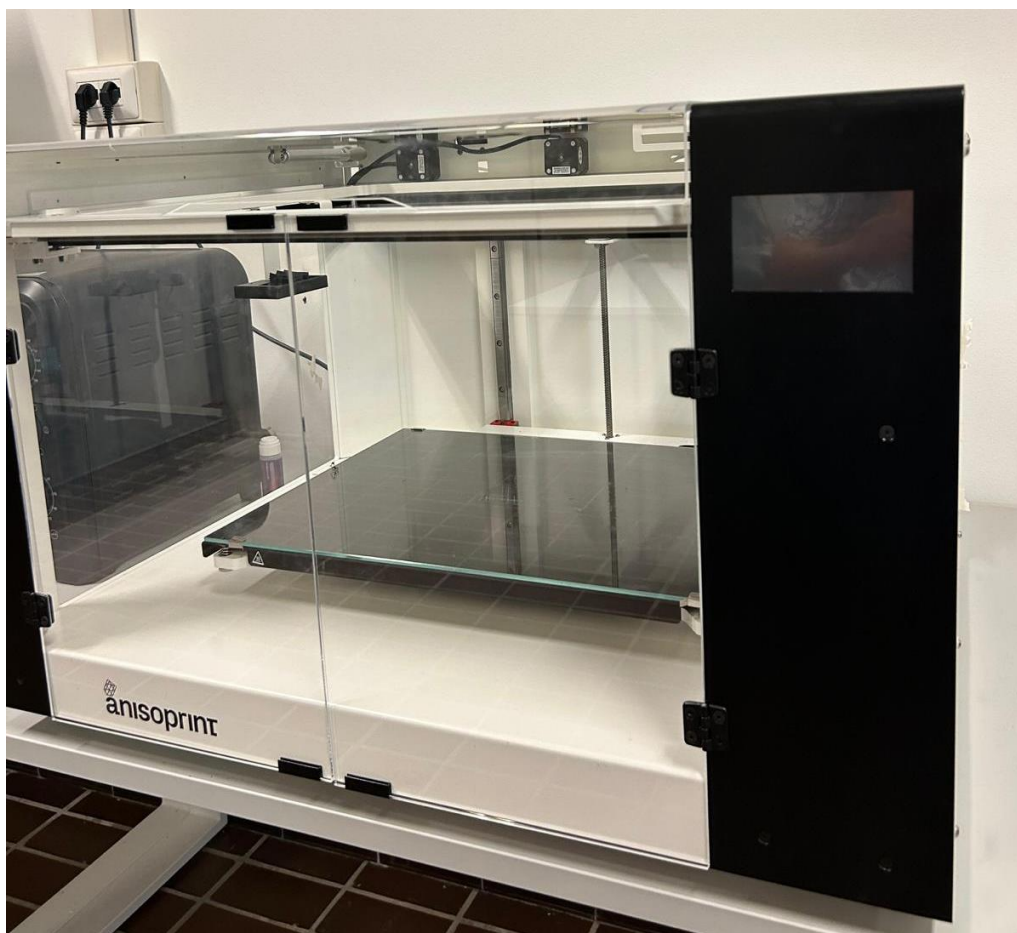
Frontale dell'Anisoprint Composer A3 con piatto di stampa e pannello di controllo
